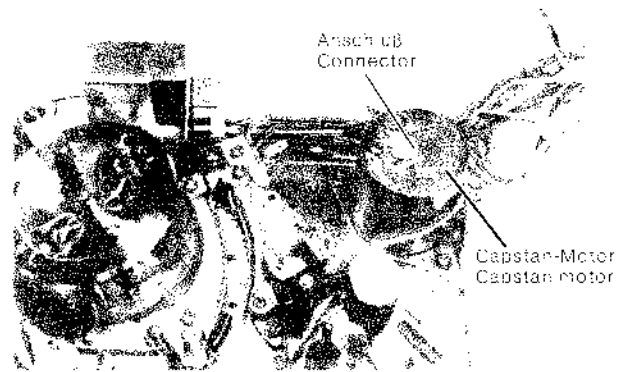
Capstan-Motor-Anschluß / Capstan motor wiring
